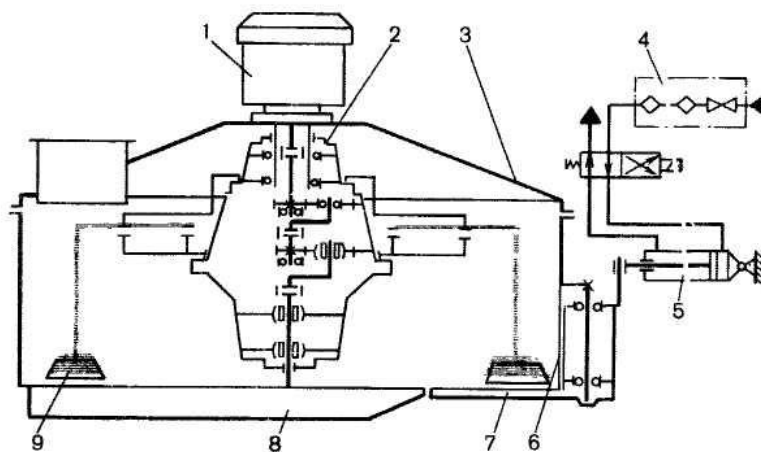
Пневмокинематическая схема смесителя СБ-146А:
